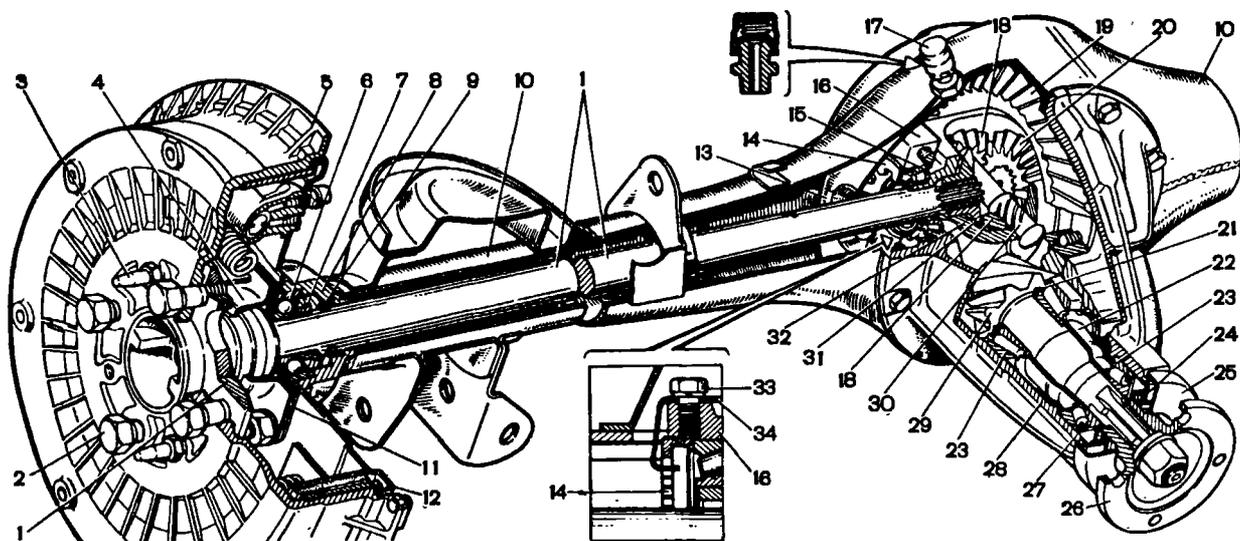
Задний мост: 1 - полуось; 2 - болт крепления колеса; 3 - направляющий штифт; 4 - маслоотражатель; 5 - тормозной барабан; 6 - подшипник полуоси; 7 - запорное кольцо; 8 - фланец балки заднего моста; 9 - сальник полуоси; 10 - балка заднего моста; 11 - пластина крепления подшипника; 12 - щит заднего тормоза; 13 - направляющая полуоси; 14 - регулировочная гайка; 15 - подшипник коробки дифференциала; 16 - крышка подшипника; 17 - сапун; 18 - сателлит; 19 - ведомая шестерня; 20 - шестерня полуоси; 21 - регулировочное кольцо ведущей шестерни; 22 - распорная втулка; 23 - подшипники ведущей шестерни; 24 - сальник ведущей шестерни; 25 - грязеотражатель; 26 - фланец; 27 - маслоотражатель; 28 - картер редуктора заднего моста; 29 - ведущая шестерня; 30 - ось сателлитов; 31 - регулировочная шайба; 32 - коробка дифференциала; 33 - болт крепления стопорной пластины; 34 - стопорная пластина гайки подшипника
